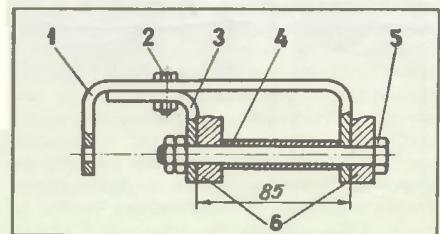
Кронштейн (в сборе) для крепления генератора переменного тока на ГАЗ-21: 1 — прежний кронштейн; 2 — дополнительный болт М6; 3 — дополнительный угольник; 4 — распорная втулка; 5 — стяжной болт; 6 — лапы генератора.
